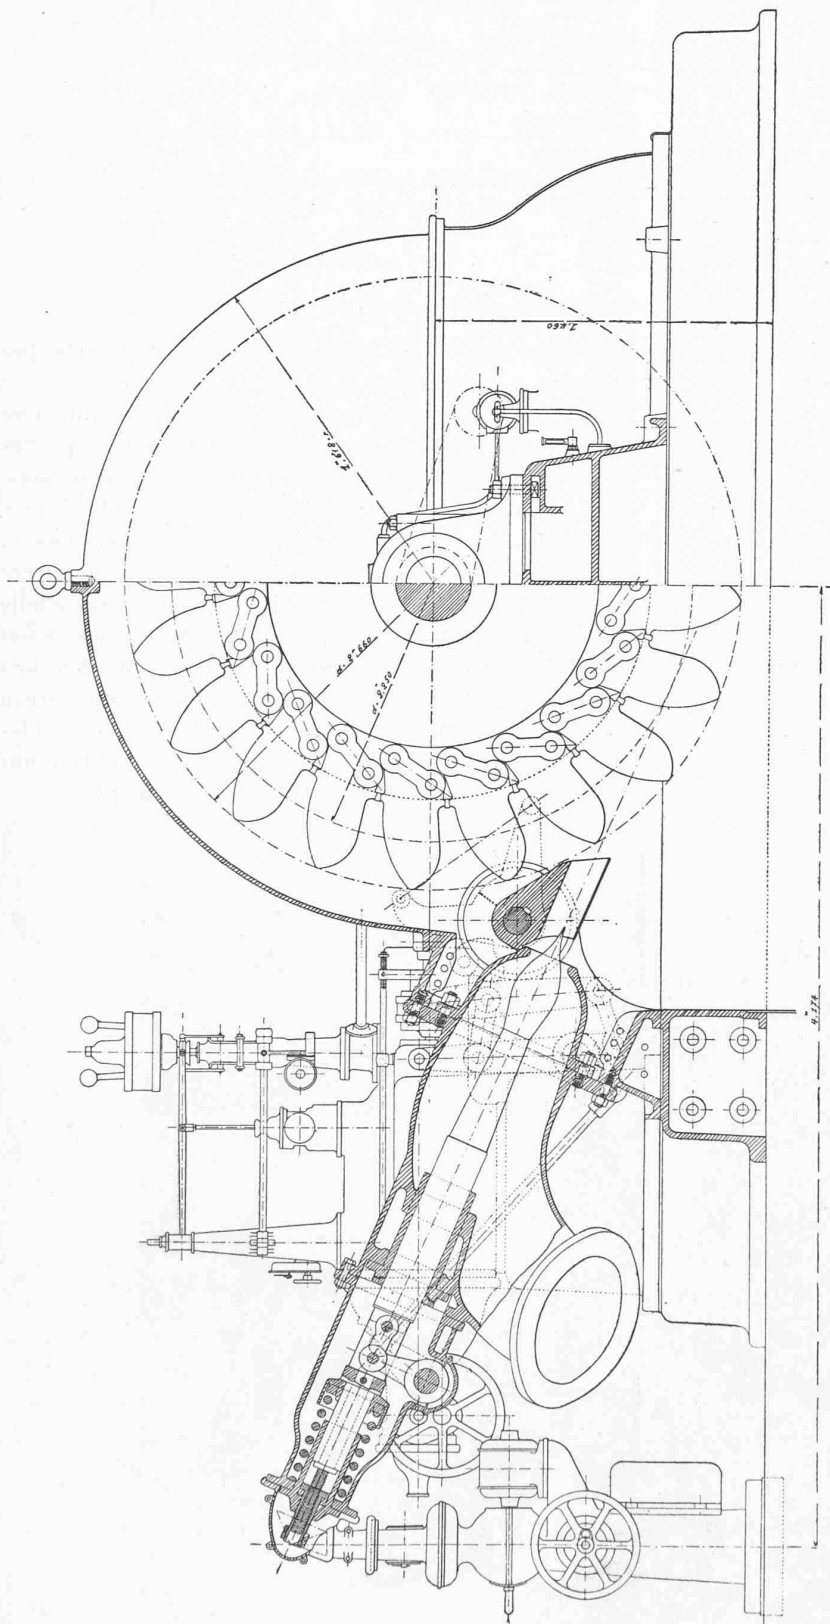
Elevation. — Coupe en travers. — 1 : 30.
